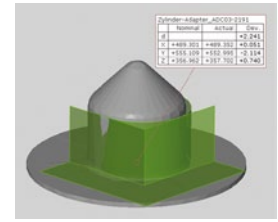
Mit GOM Adapter gemessenes Geometrie-element (Zylinder)
